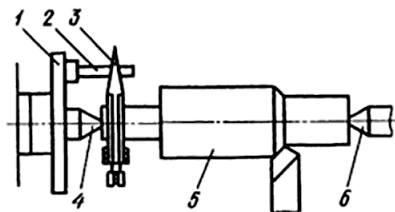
Установка заготовок в центрах с поводковым патроном
